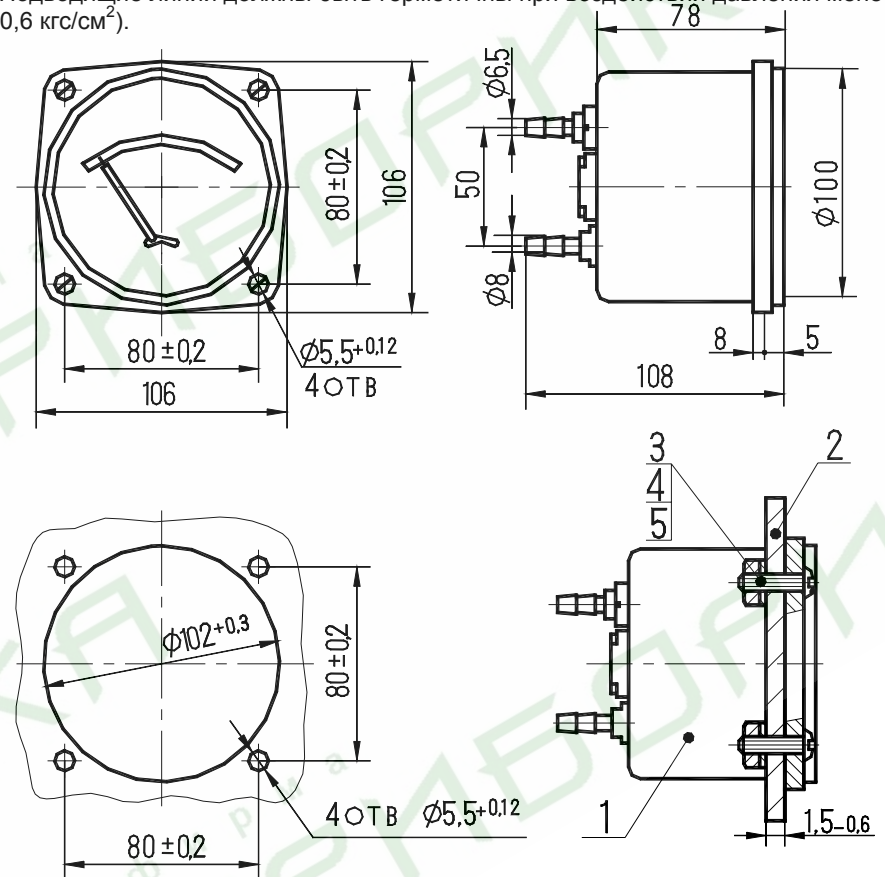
Габаритные и присоединительные размеры приборов:
